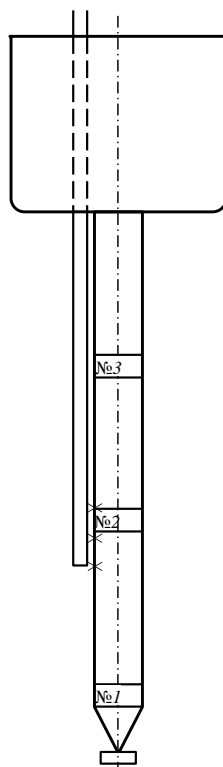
Схемы установки термопар на керамической форме и резки заготовки под образцы
